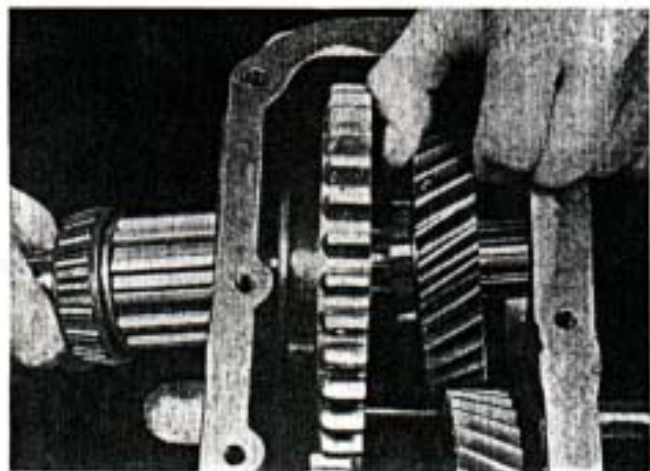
Ubicando el engranaje del eje principal, en éste.
